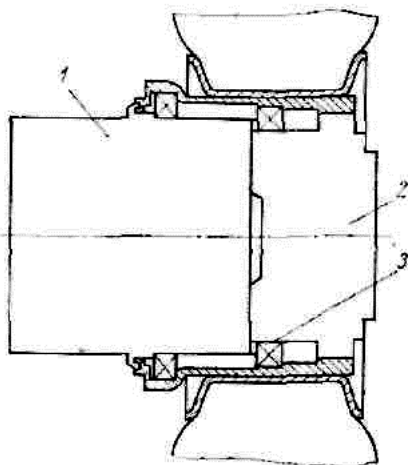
Схема мотор-колеса при компоновке VI вида
